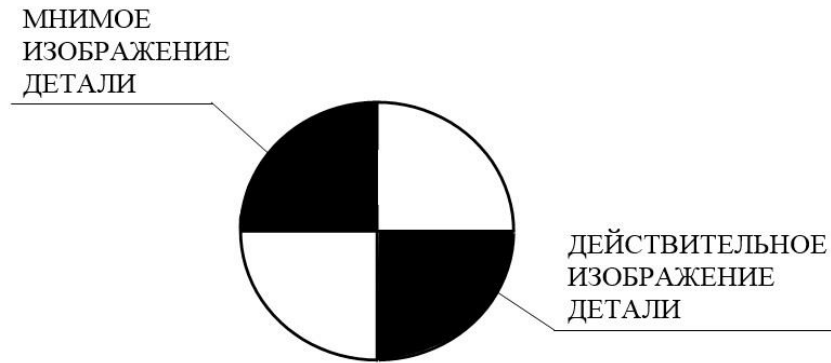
Определение координат вершины заготовки при помощи головки двойного изображения
